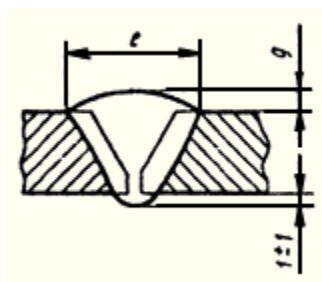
Конструктивные элементы сварного шва соединения С17 по ГОСТ 14771-76.
